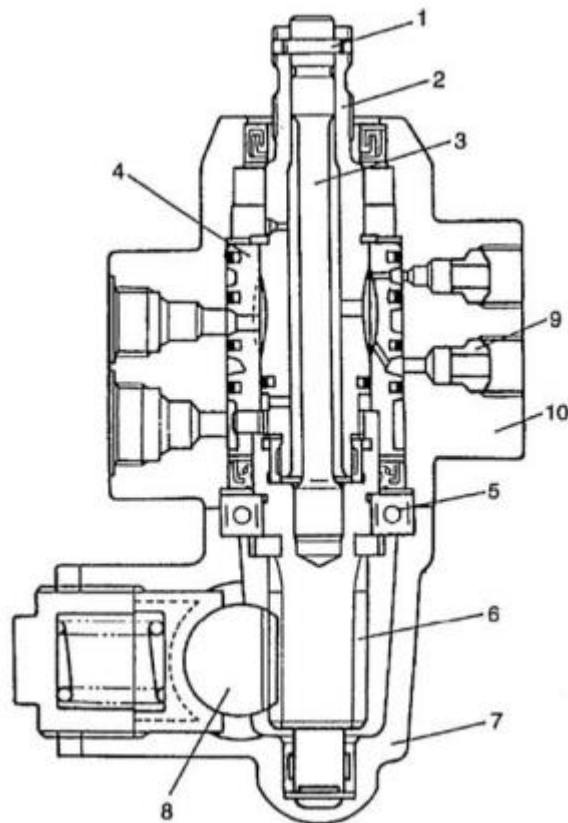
Пристрій ГПК: 1 - штифт; 2 - золотник; 3 - торсіон; 4 - обойма золотника; 5 - підшипник; 6 - шестерня; 7 - корпус кермового
